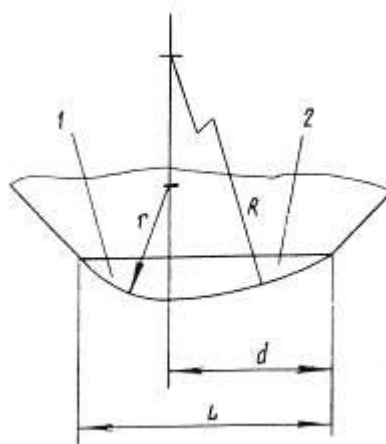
Форма заточки выглаживающего инструмента с разными радиусами
